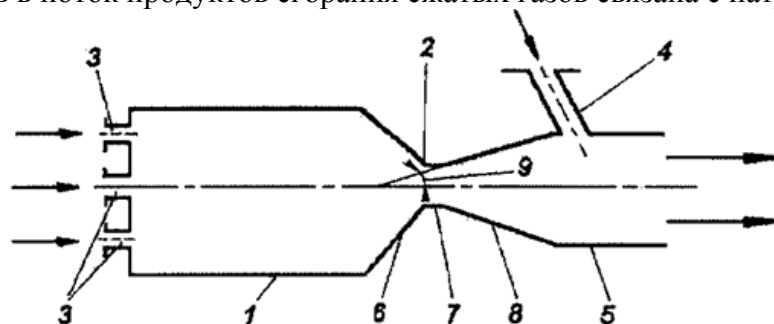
Схема устройства для сверхзвуковой газопорошковой наплавки.
